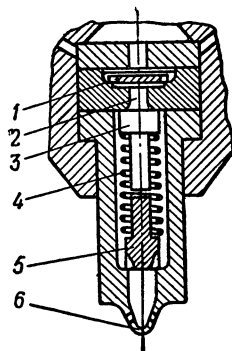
Схема открытой форсунки дизеля ЯАЗ-204:
